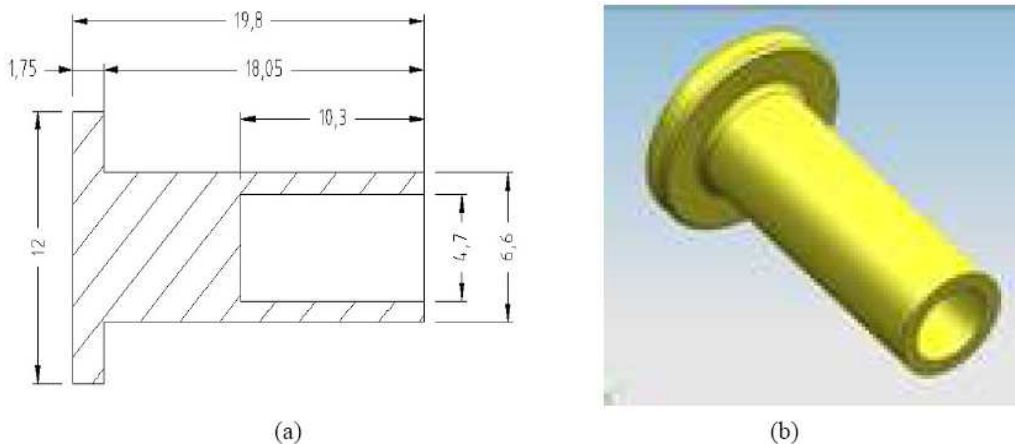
Fixador atual: (a) dimensões básicas; (b) vista isométrica.
